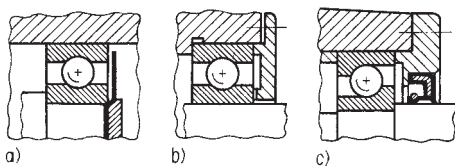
Dichtungen für Wälzlager (s. auch Abschnitt 7.6)
